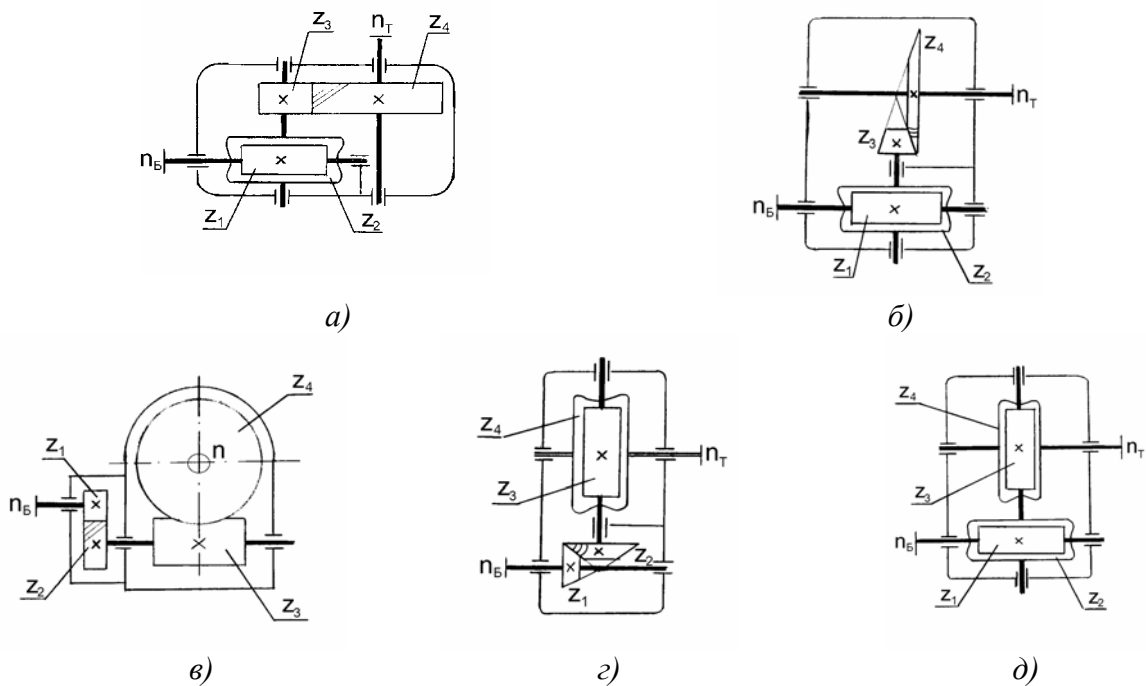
Двухступенчатые редукторы с червячной передачей
